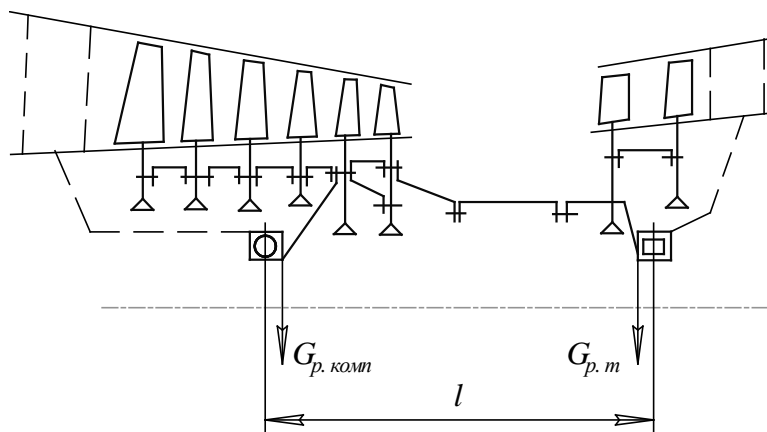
Ротор с навесными ступенями и размещением опор в плоскостях центра масс роторов компрессора и турбины
